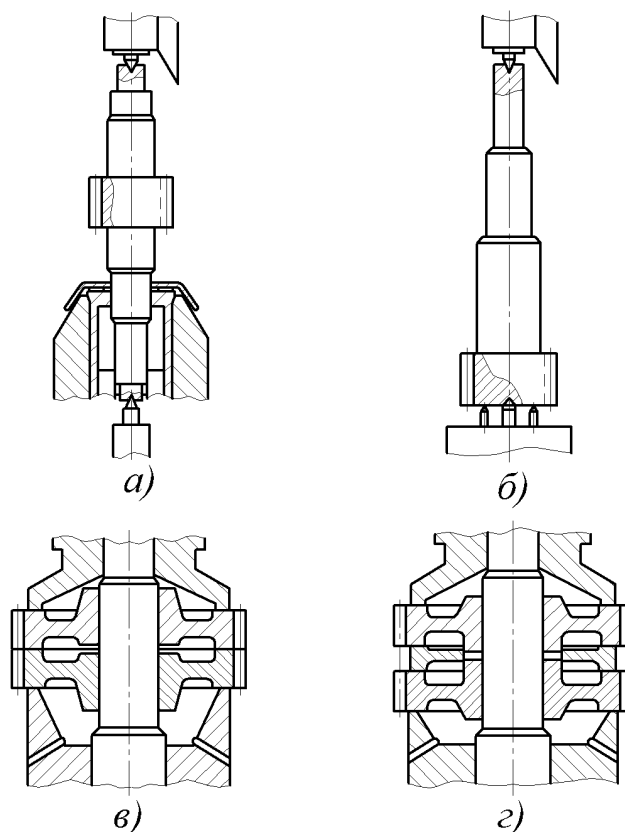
Види базування заготовок зубчастих коліс
